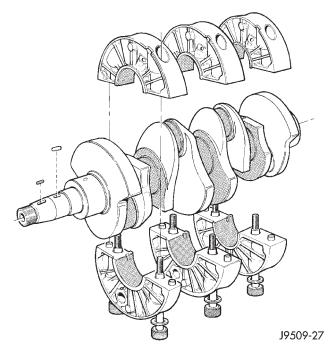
Conjunto do Eixo de Manivela e Mancal do Suporte
